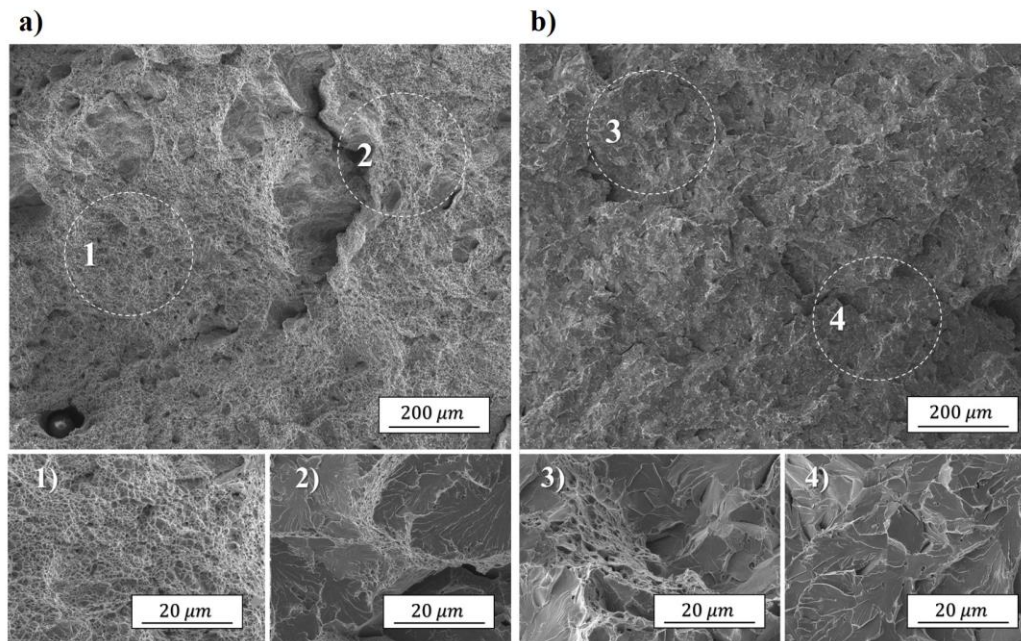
Imágenes de MEB; a) metal base; b) cordón de soldadura.
